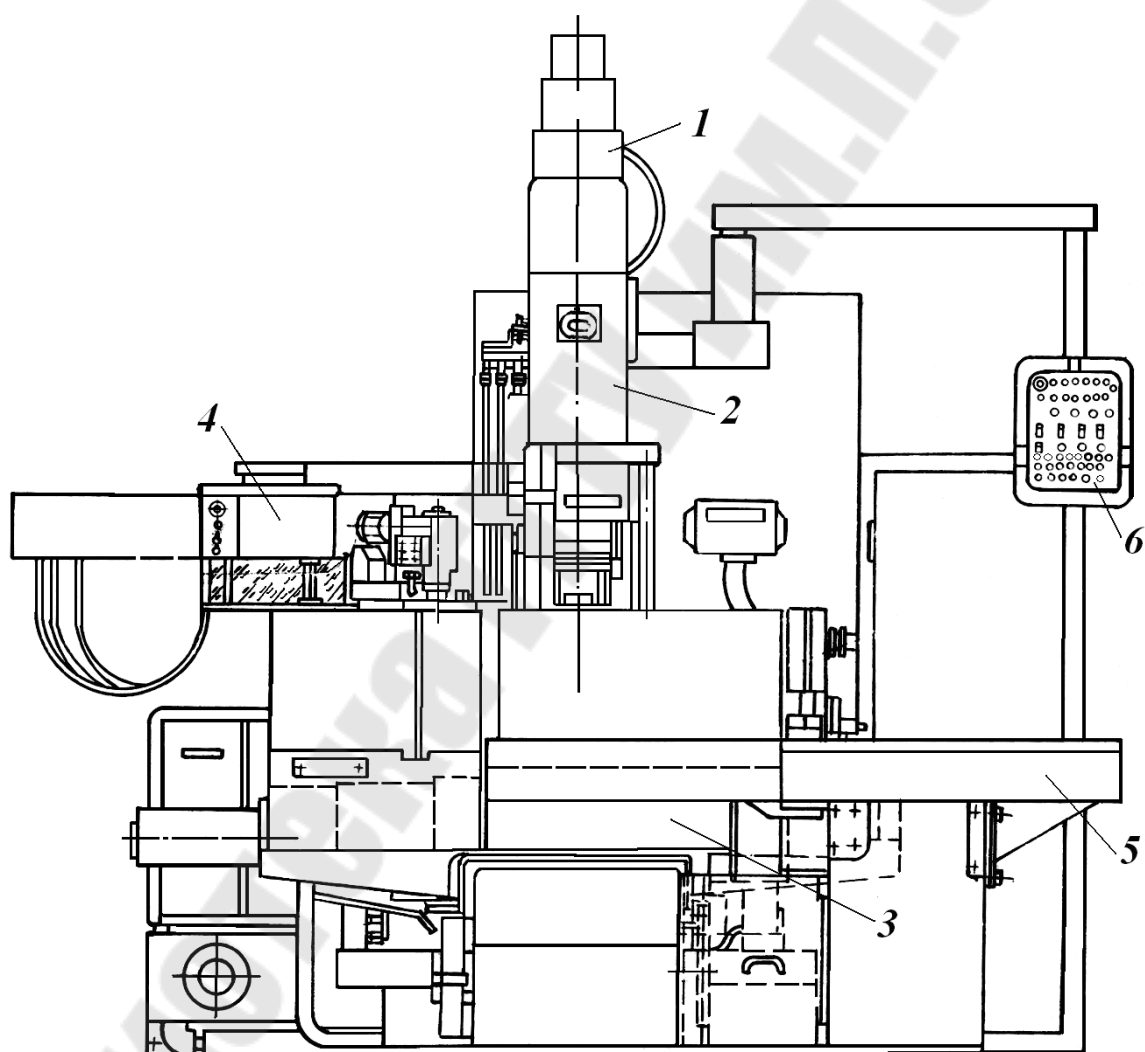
Эскиз общего вида станка 21104П7Ф4
